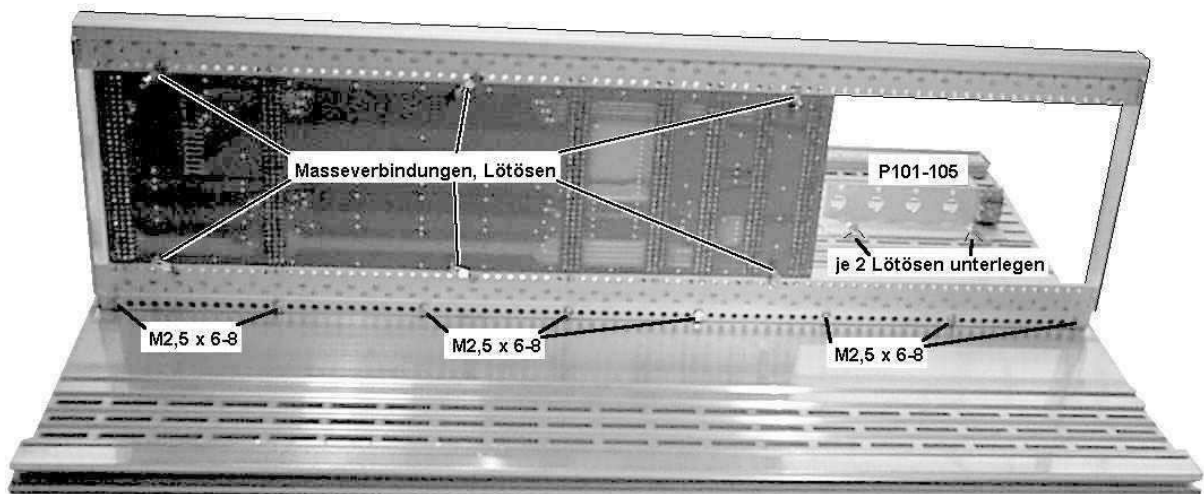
Montage der Grundplatte und des Verdrahtungsrahmens
